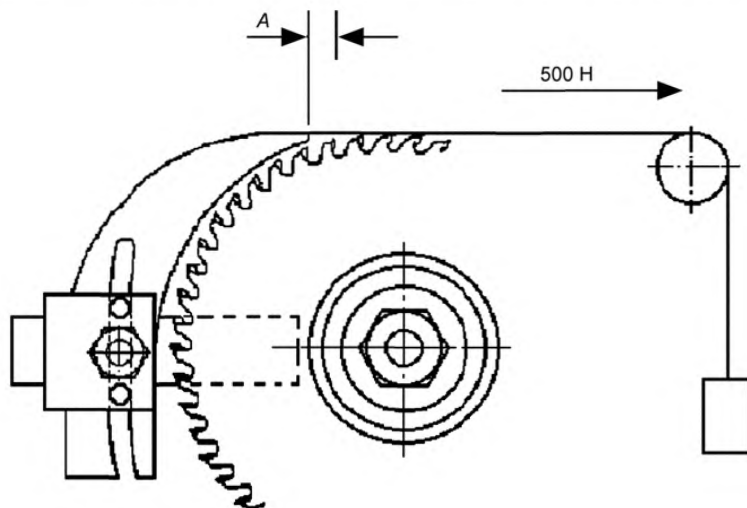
Испытание прочности крепления расклинивающего ножа
